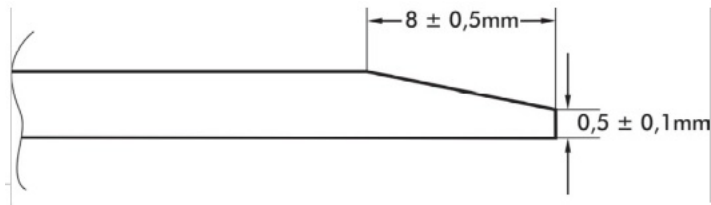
Dimensões do chanfro desquinado tipo sobreposto
